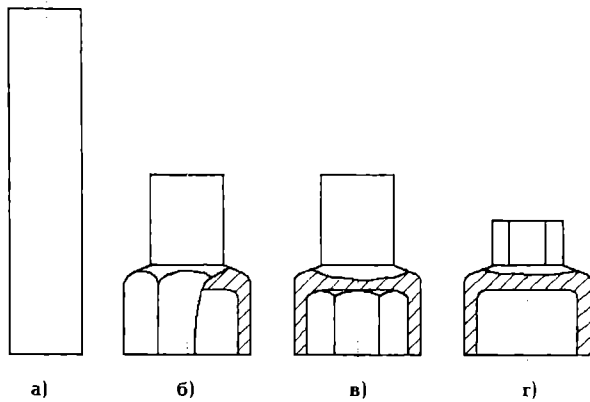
Изделия типа Иг, Ид, Пд (б, в) и Шд (г), которые возможно получать поперечно-прямым выдавливанием из цилиндрической заготовки (а)
